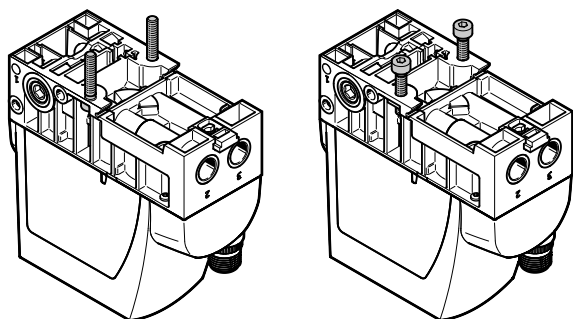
Befestigung über Ventilunterseite mit Schrauben M4/Schrauben M4 und
